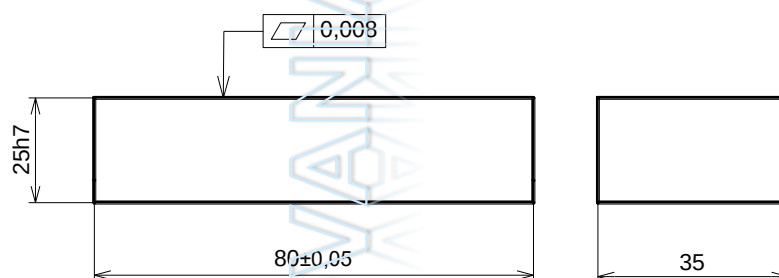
Tolerancia priamosti v priestore – príklad
